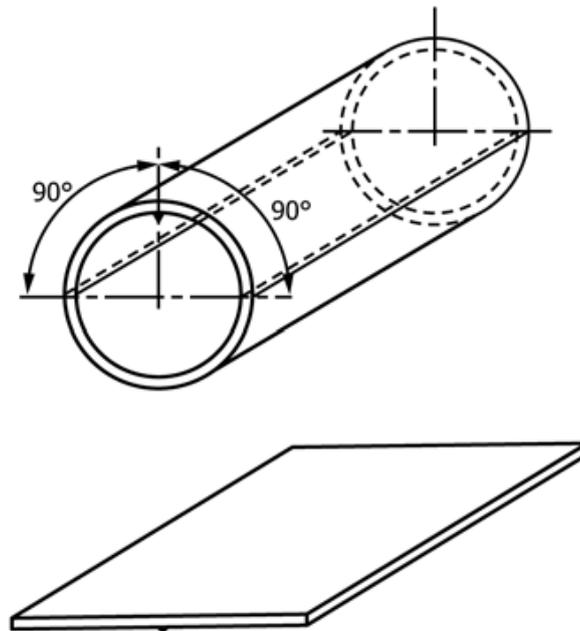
Образец для испытаний на сплющивание обратной поверхности
